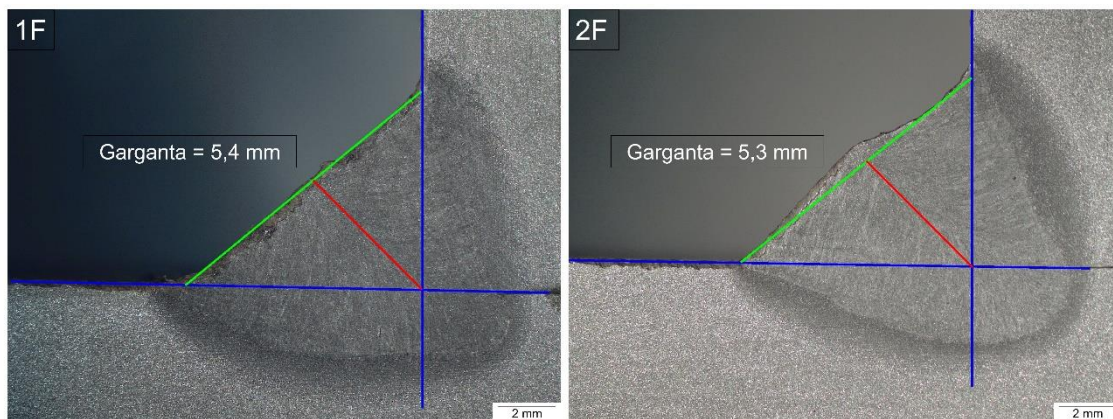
Aspectos dimensionais da garganta do cordão de solda para testes in loco considerando cordão a5 nas posições 1F e 2F soldados após redefinição dos parâmetros de solda conforme Tabela 11.
